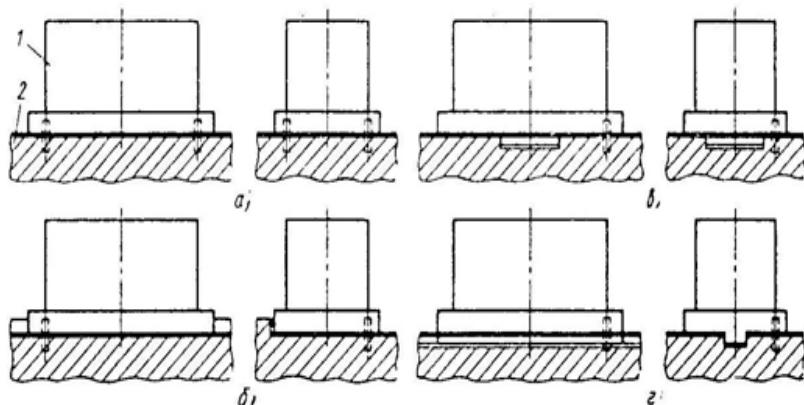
Схемы сборочных единиц, детали которых базируются на плоскостях
